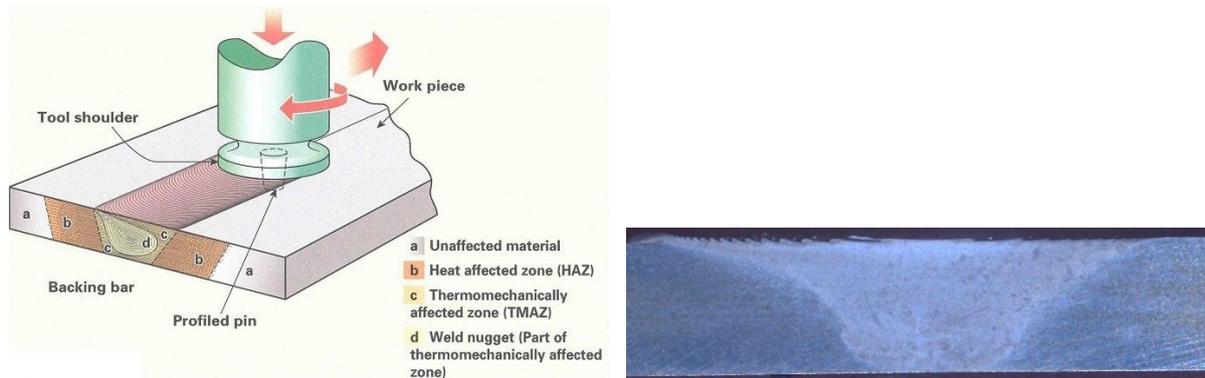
Esquema cordón de soldadura FSW [TWI Global] e imagen metalográfica.
